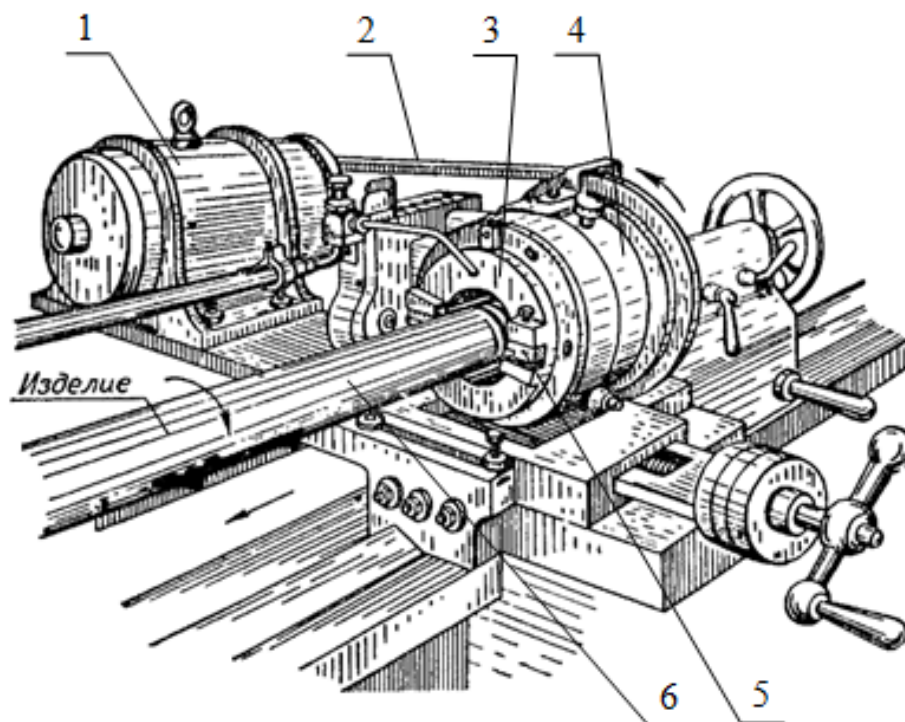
Общий вид приспособления для вихревого нарезания резьбы [9].
